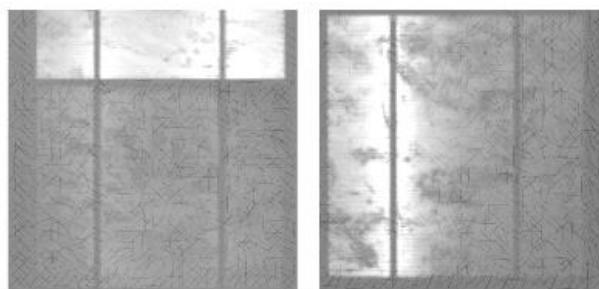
Imágen por Electroluminiscencia (EL) de un módulo con defecto por brillo ocasionado por mala soldadura
